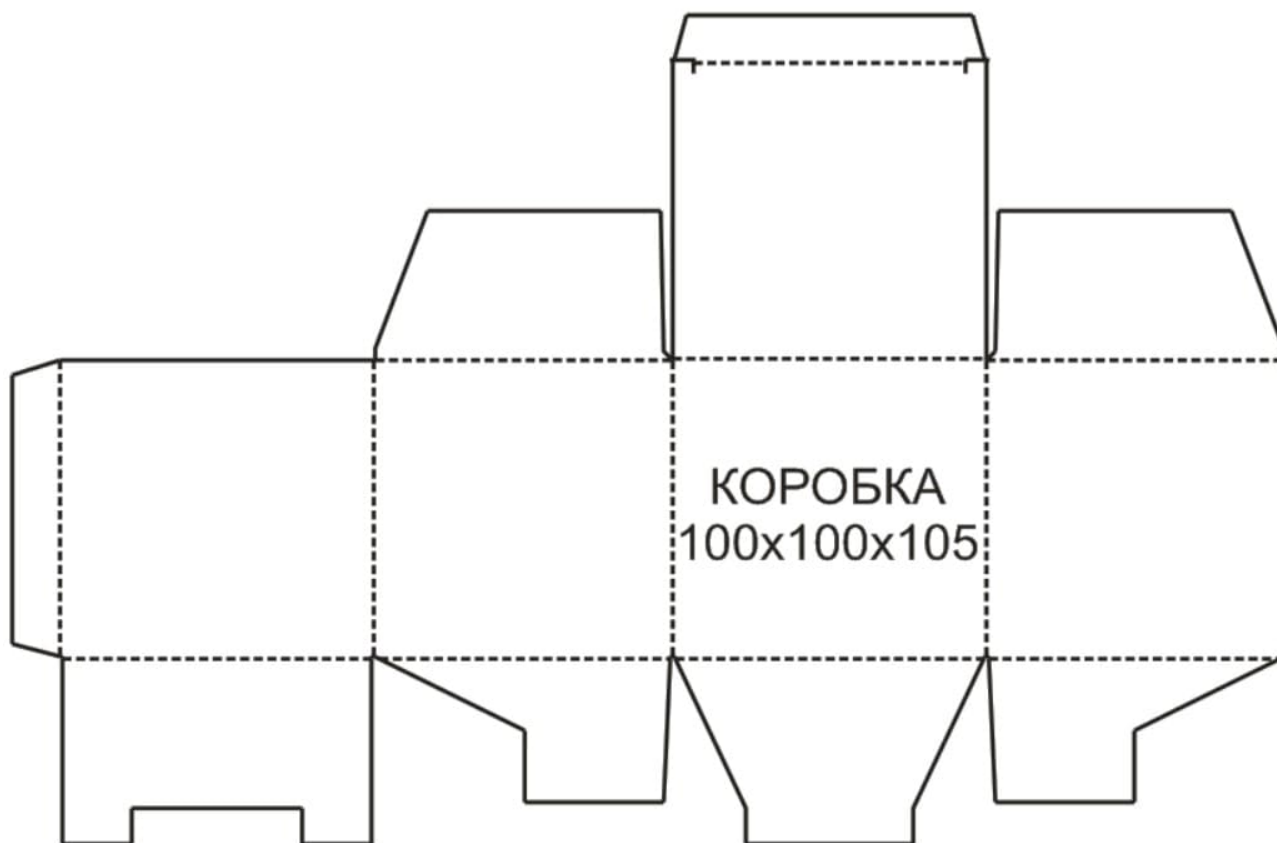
Чертеж выкройки коробки с одной склейкой и самосборным дном
